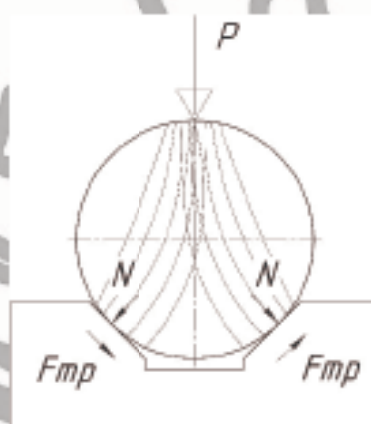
Сили, що виникають при затисканні заготовки
